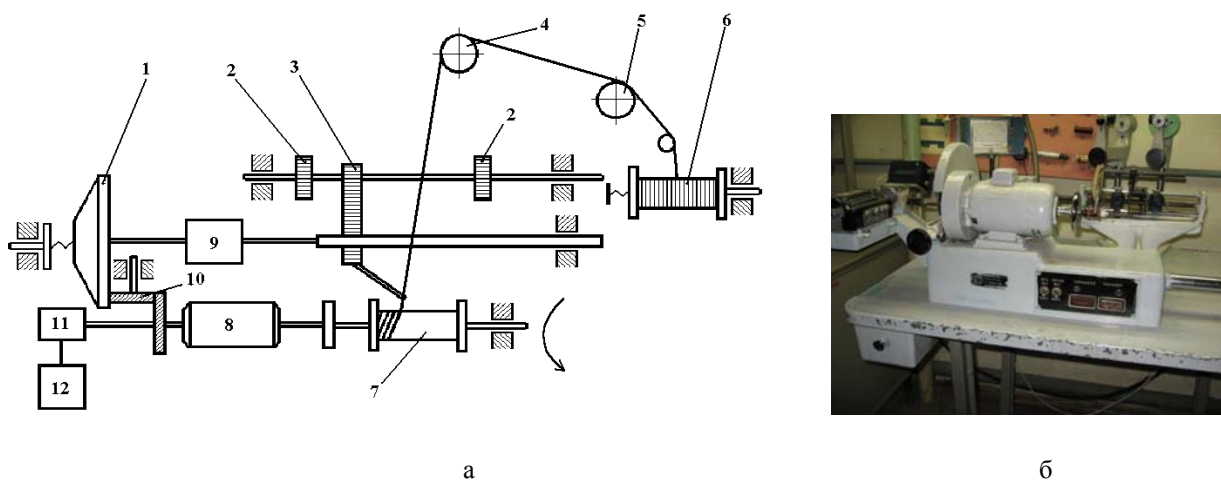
Кинематическая схема (а) и внешний вид (б) намоточного станка
